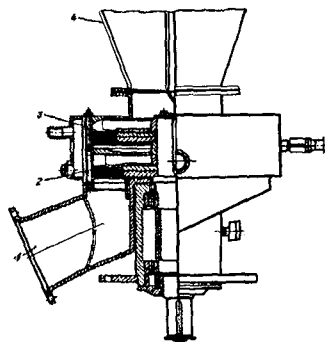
Гомогенизатор дискового типа: 1 – сливной патрубков; 2 – подвижной диск; 3 – неподвижный диск; 4 – приемная воронка.
